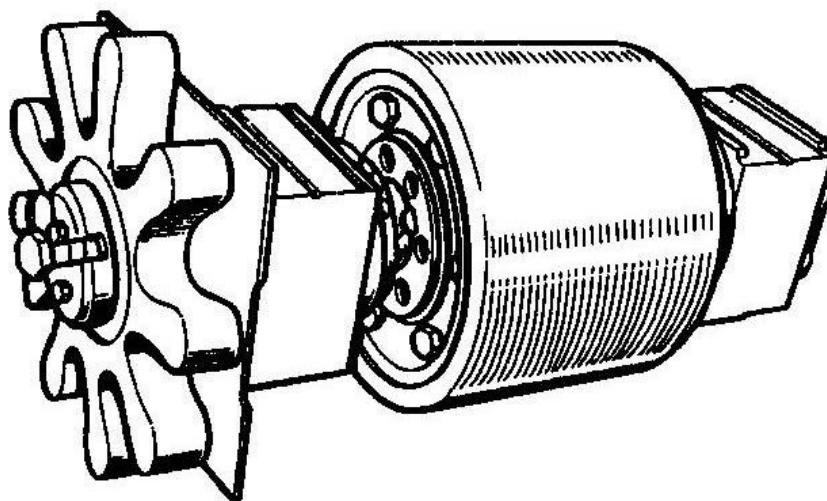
Гладкий валок в сборе с шестерней с удлиненными зубьями
